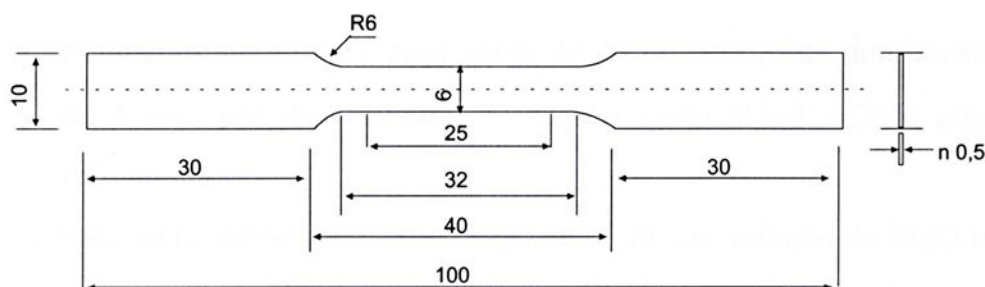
Forma e dimensões dos corpos de prova em milímetros.
